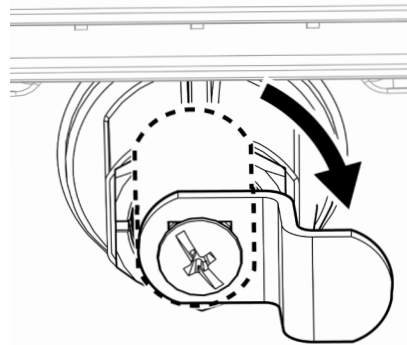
soporte en L en la posición desbloqueada; paralelo al borde de la tapa del accesorio
